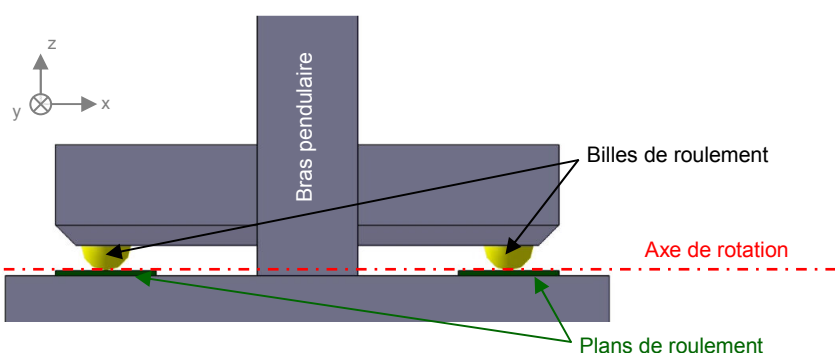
Principe d'un pivot constitué d'une paire de billes reposant sur un plan de roulement
